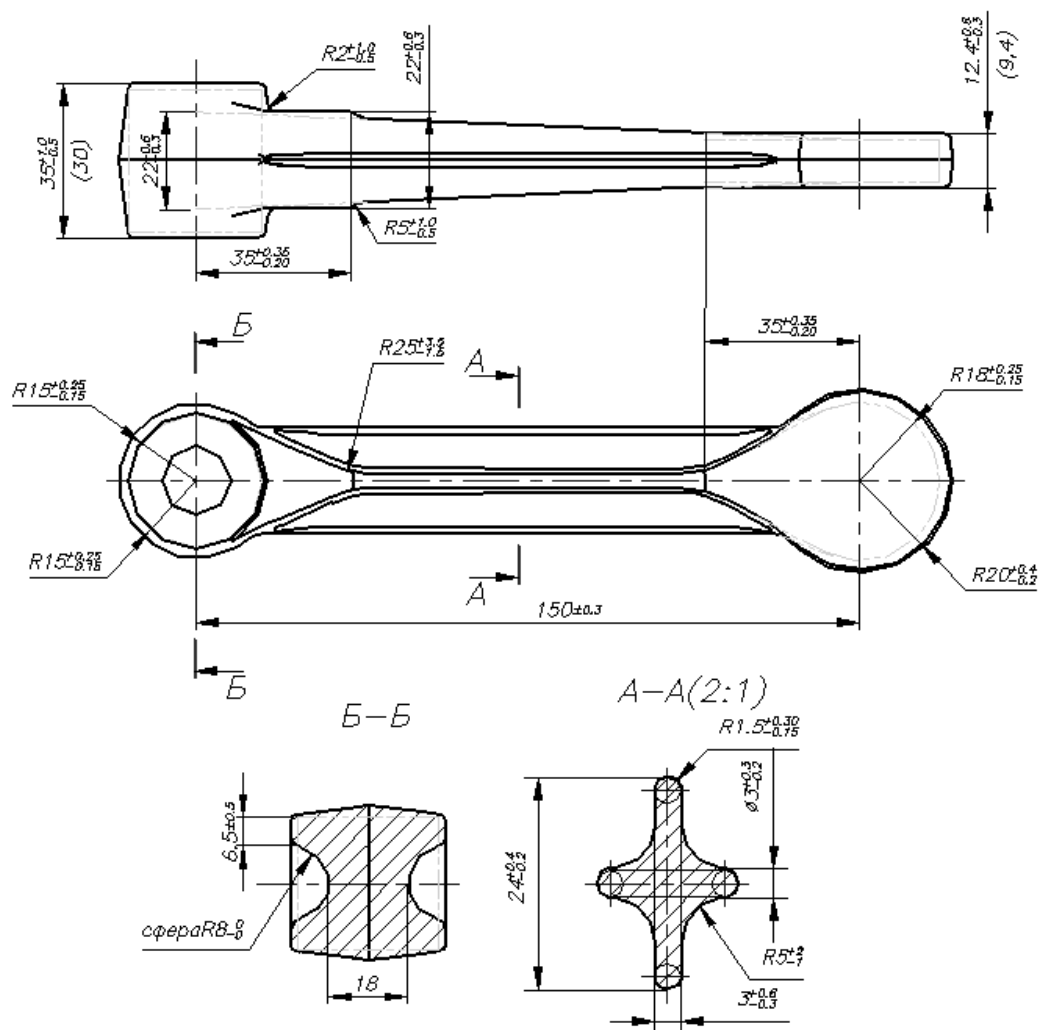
Чертеж штампованной поковки «Рычаг»
